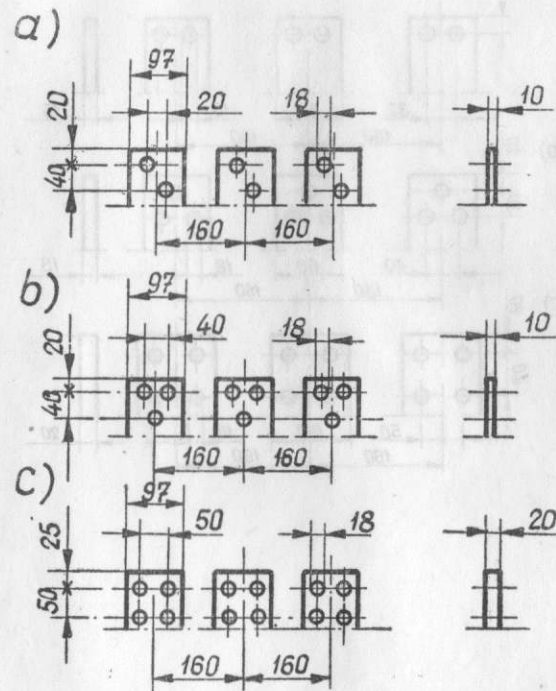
Размеры главных зажимов выключателя АРУ-50WA
